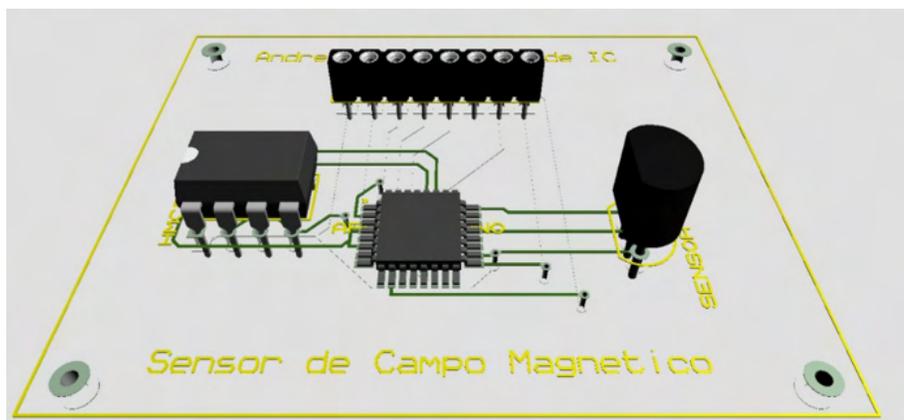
Visualização 3D de Sensor de Campo Magnético – Frontal.
